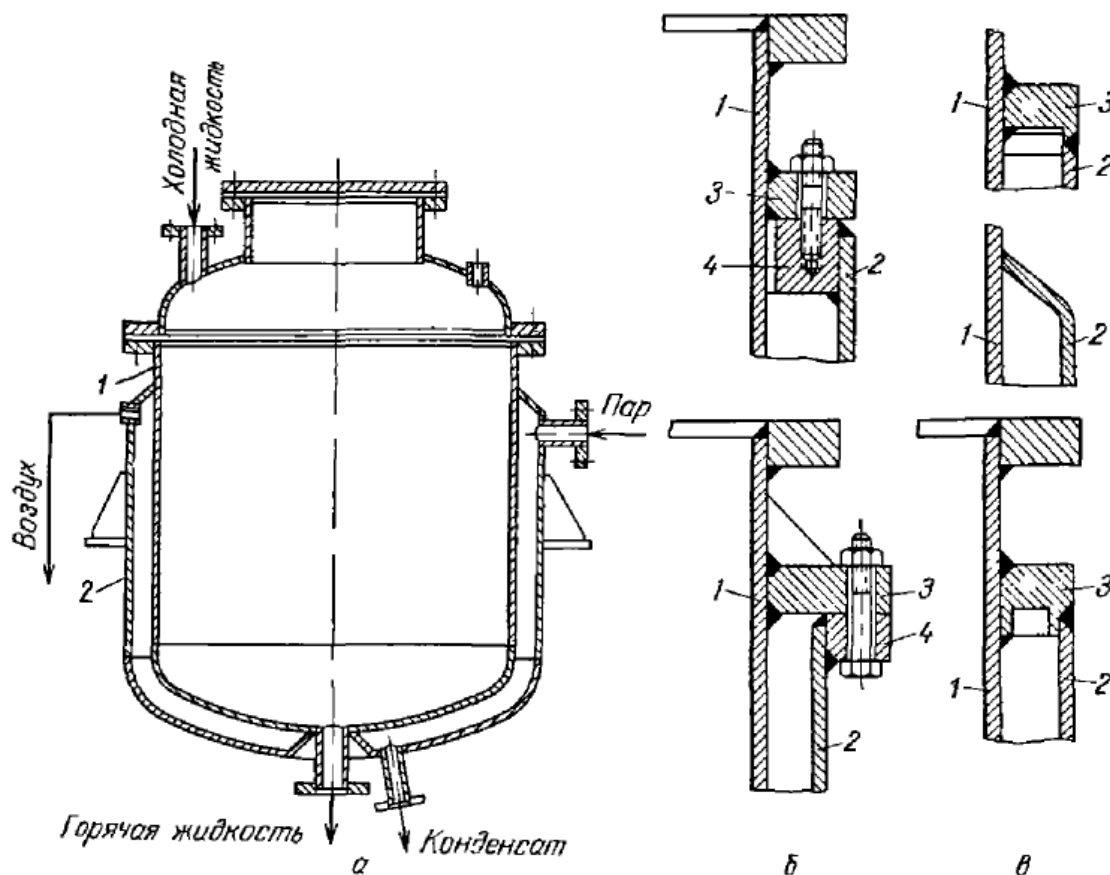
Аппарат с греющей рубашкой (а) и способы её присоединения (б – фланцевое, в – сварное):
